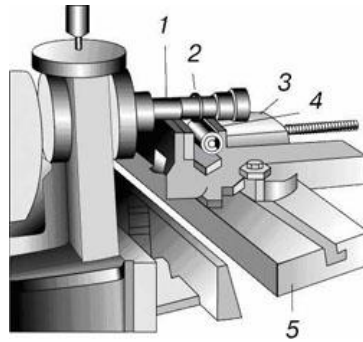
Фрезерний верстат, різання канавки шпонки на невеликому валу: 1 - оправлення; 2 - фреза; 3 - лещата; 4 - деталь; 5 - стіл
